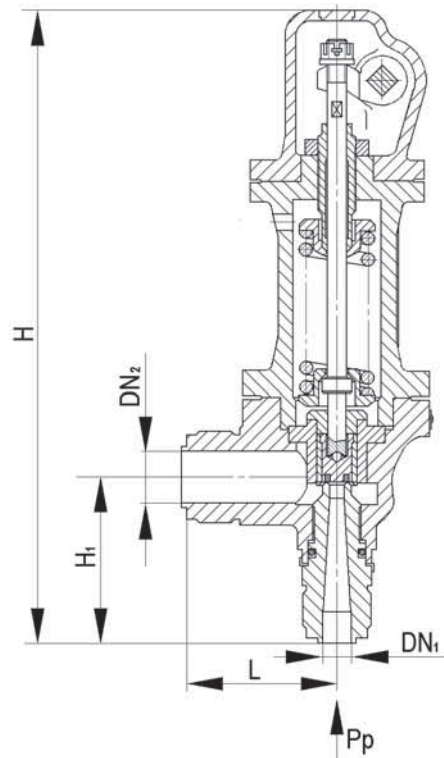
Клапан предохранительный полноподъемный штуцерный
